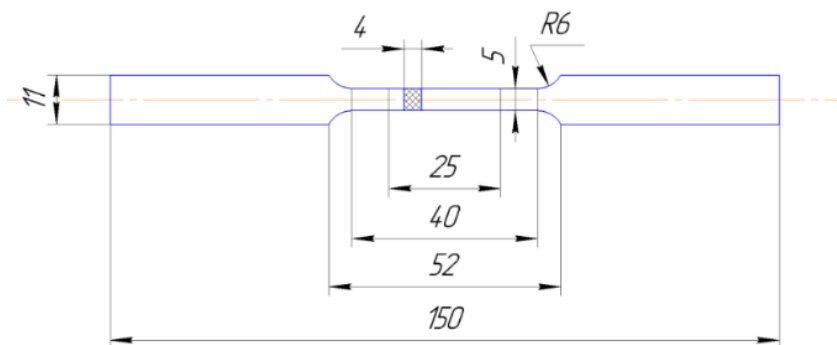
Форма и размеры образца для испытаний на прочность при растяжении
